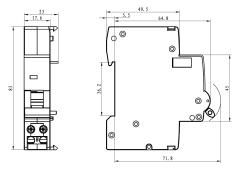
Внешний вид и габаритные размеры аксессуаров SMARTWATT PDE LCB-MX.
